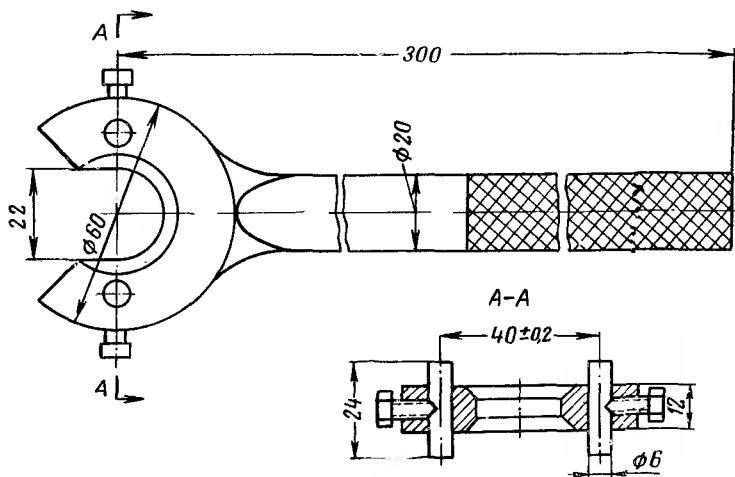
Ключ для затяжки гайки резервуара телескопических амортизаторов
